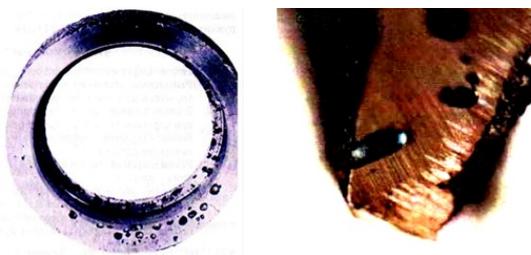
Отливка «Фланец» с раковиной сферической формы, поверхность раковины имеет цвета побежалости
